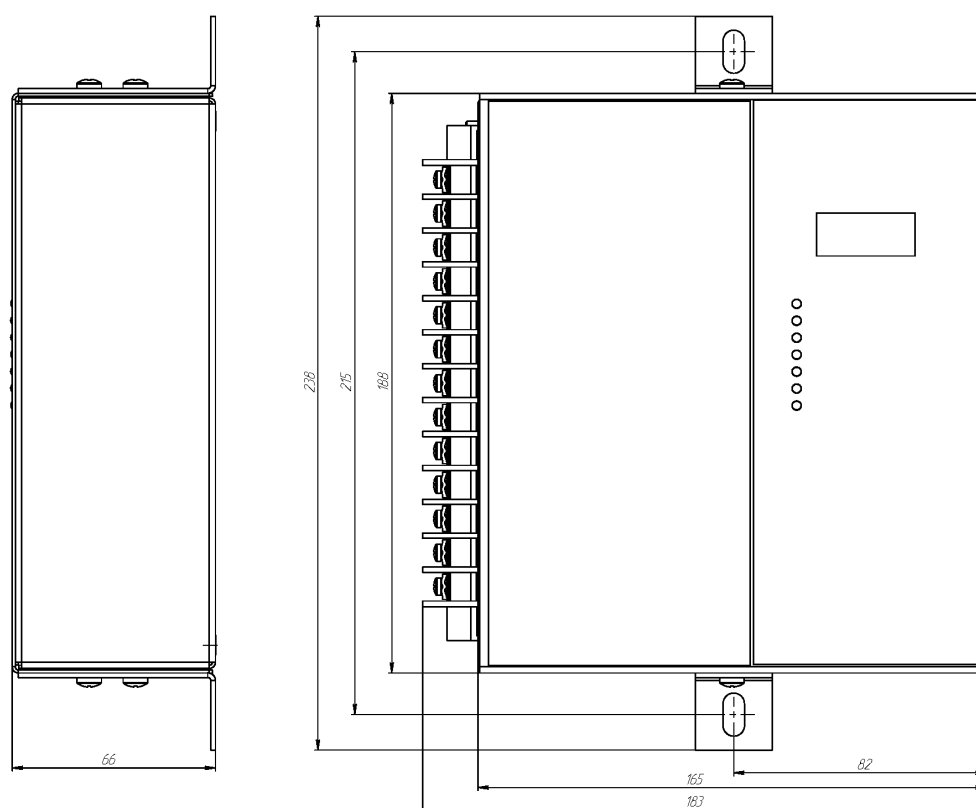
Габаритные и установочные размеры REST.02m в корпусе «Ш».
